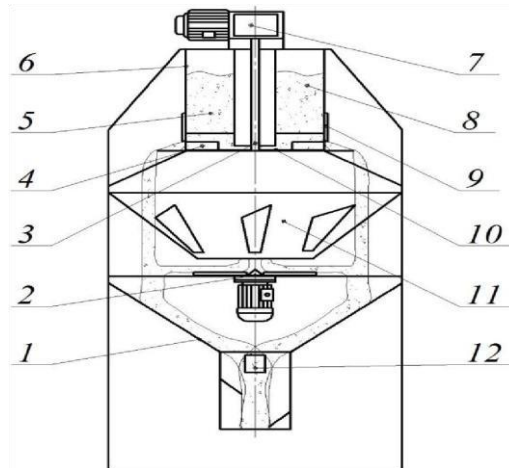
Схема дозатора-смесителя сыпучих кормов: 1 – вторая воронка; 2 – разбрасыватель; 3 – приводной вал; 4 – скребок; 5 – подвижная перегородка; 6 – бункер; 7 – мотор-редуктор привода скребков; 8 – неподвижная перегородка; 9 – манжета; 10 – диск; 11 – первая воронка; 12 – пластины
